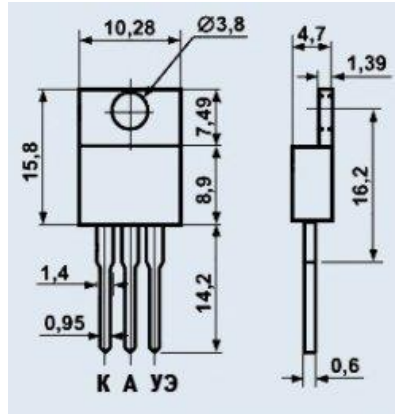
Габаритні розміри ТС106-10 "Протон"
